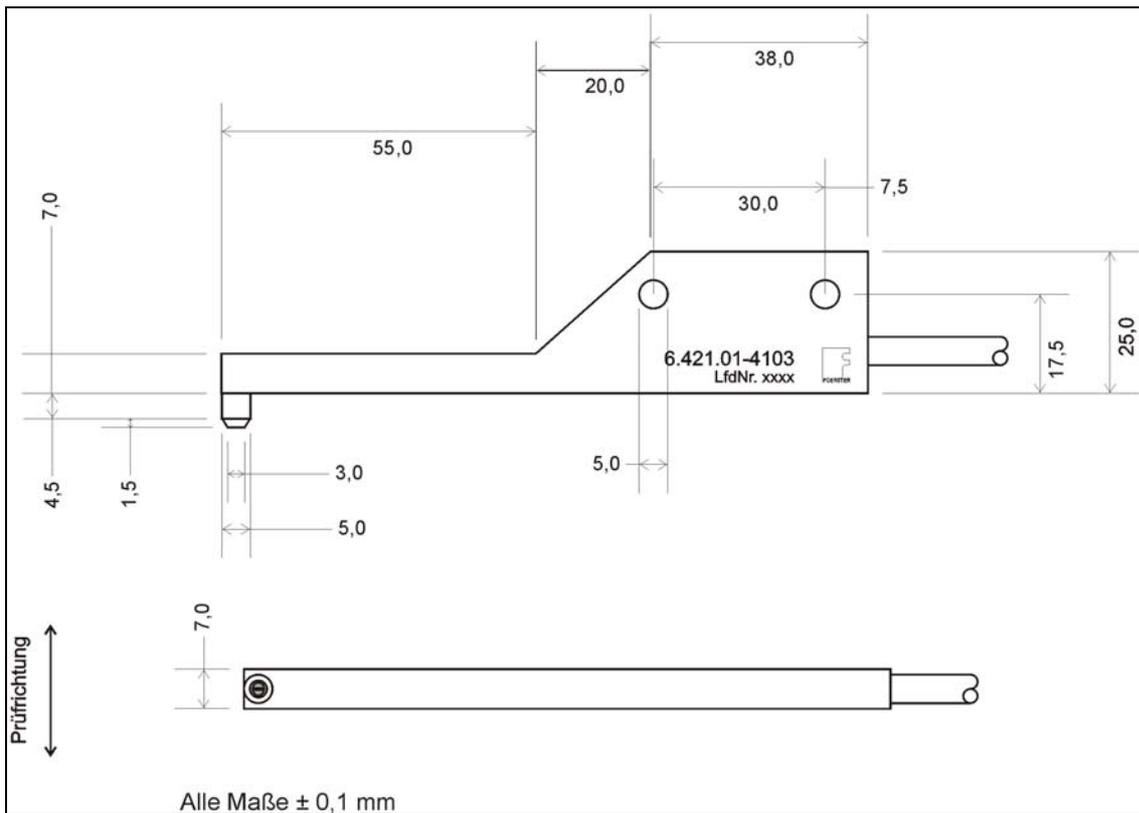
Taster abgewinkelt 90 D, AK 6.421.01-4103.
